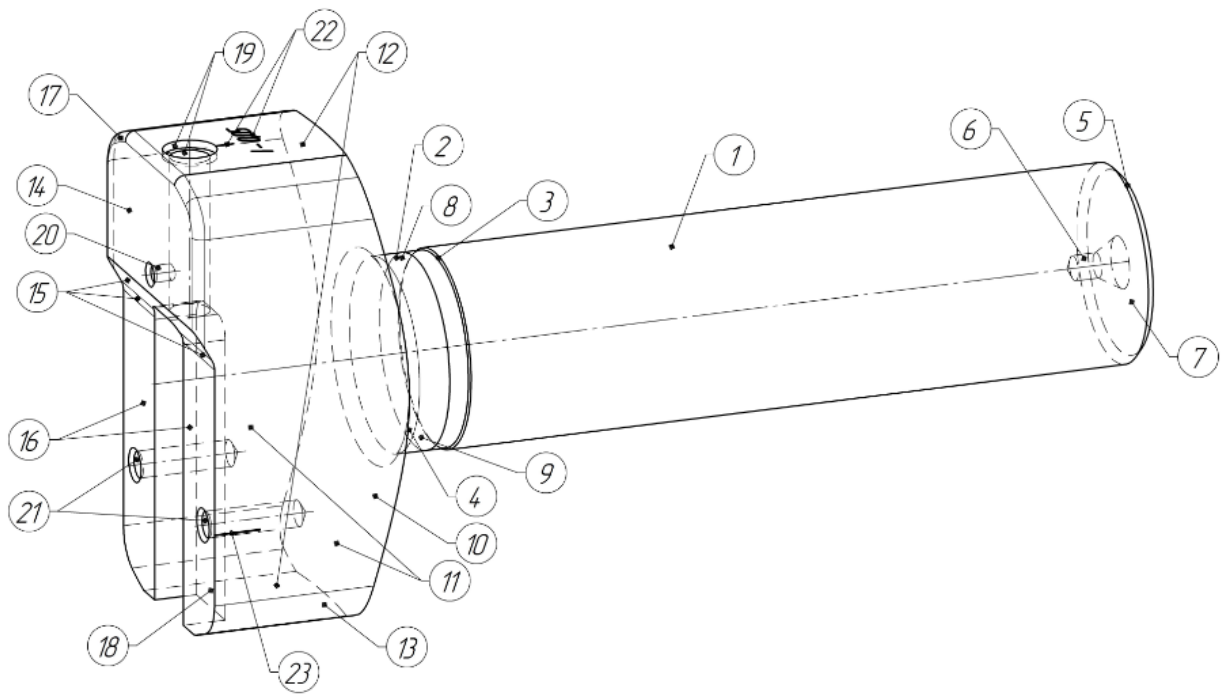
Поверхні корпусу інструменту, над якими треба виконати механічну обробку
